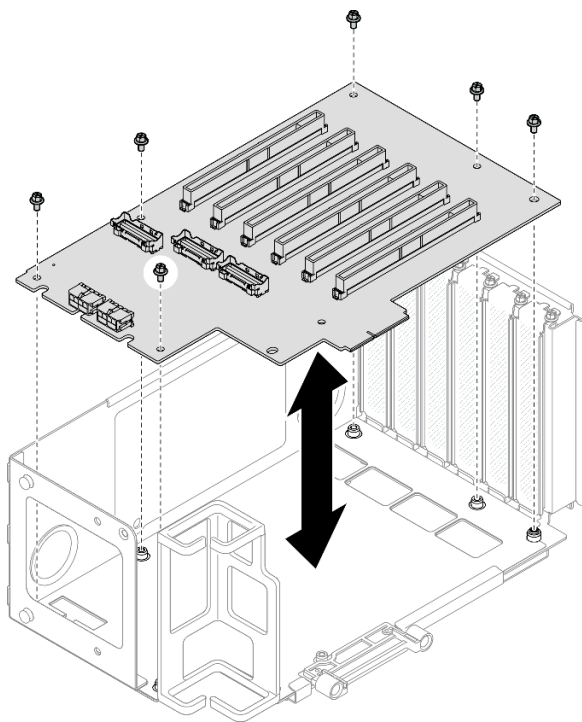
Removendo o cartão da placa riser PCIe da placa riser
